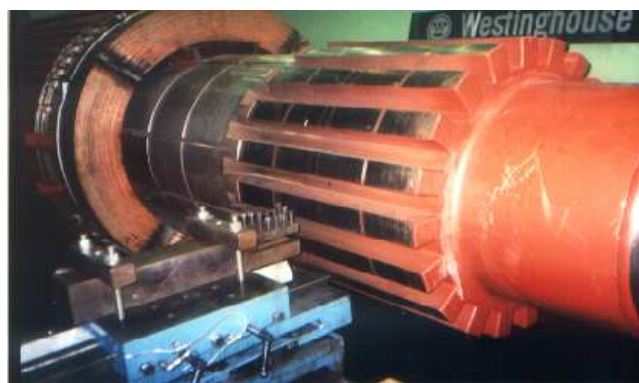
Dispositivo de corte e o alívio de tensão no corpo do rotor.
